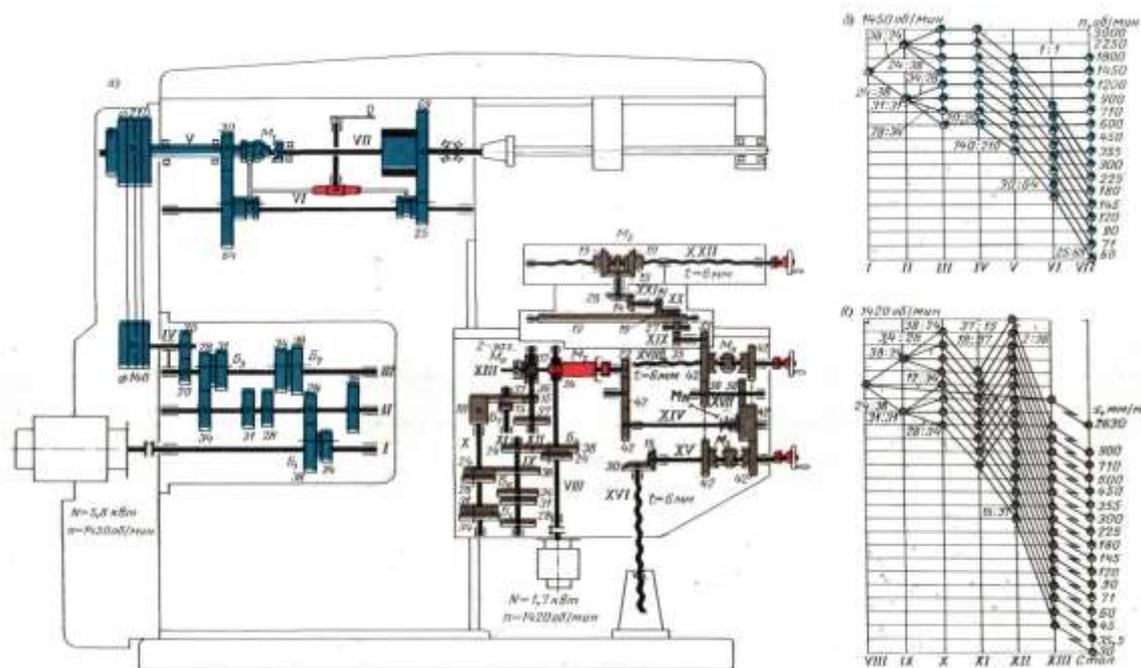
Кинематическая схема универсально-фрезерного станка модели 6H81.
